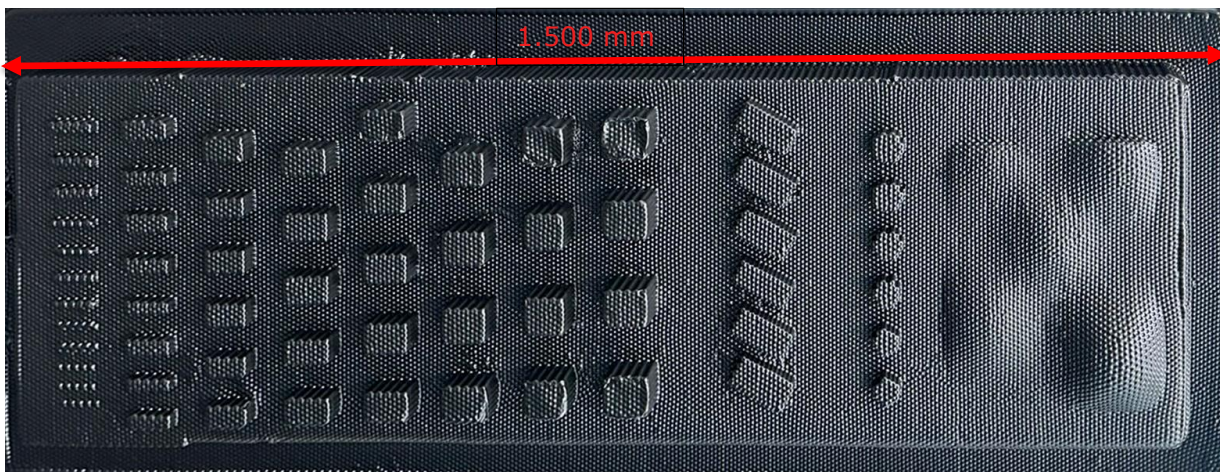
Formteil der Testgeometrie für das Stifbettwerkzeug.
